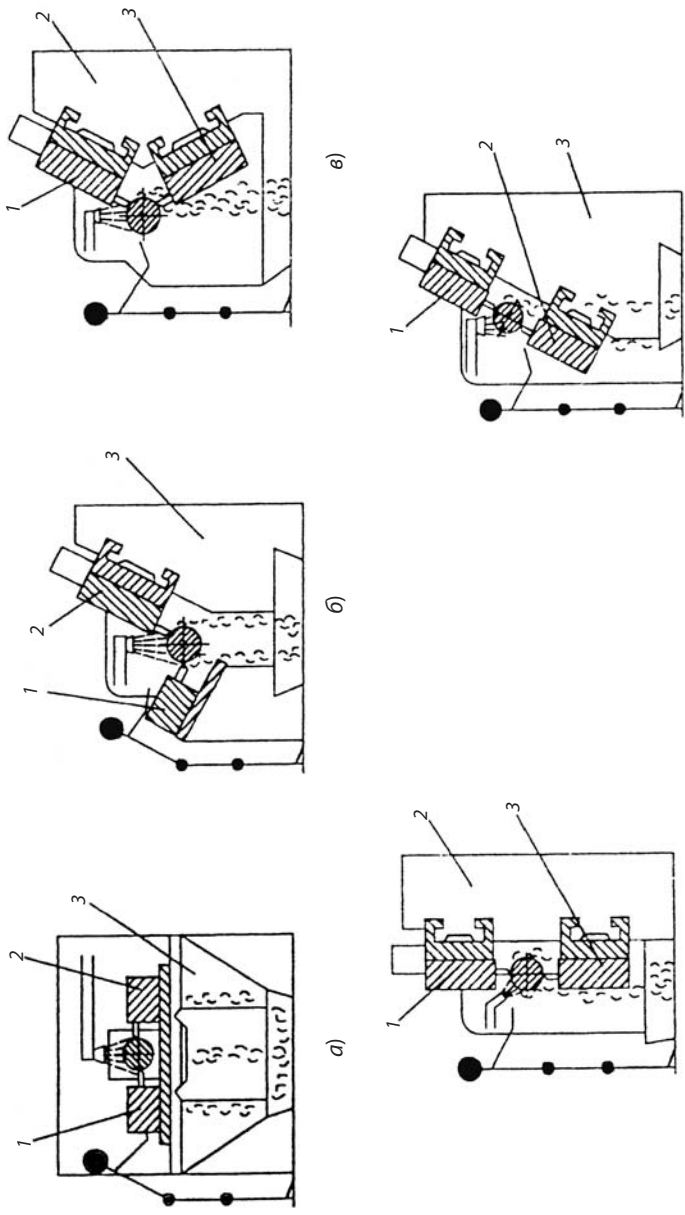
Варианты компоновки станины и суппортов в токарных станках:
